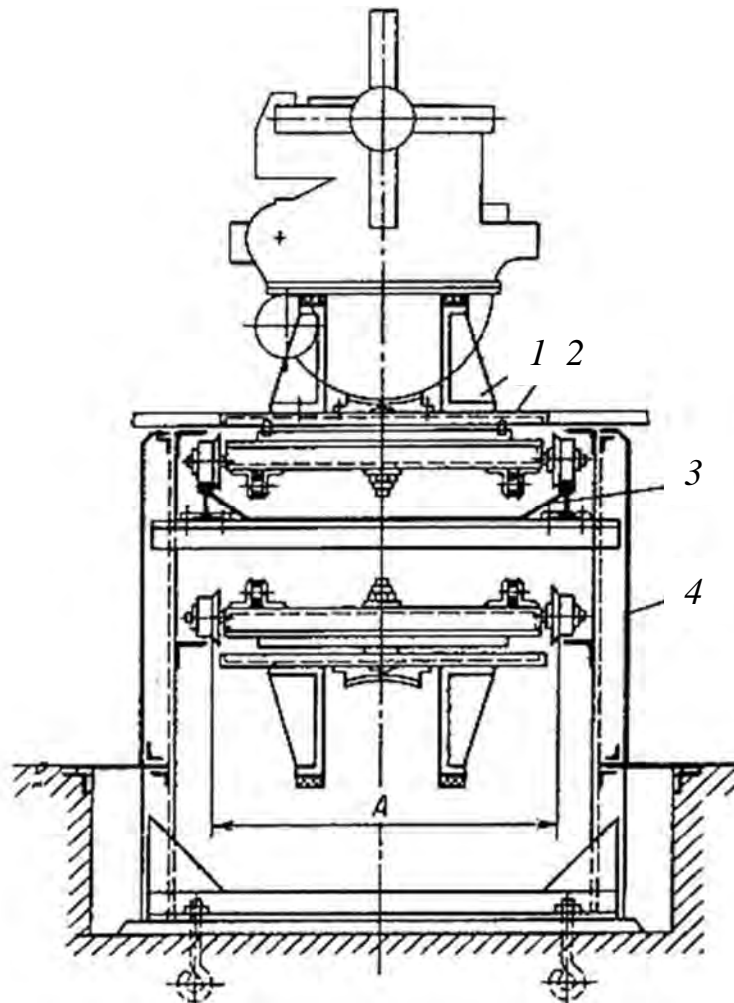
Конвейер с опрокидывающимися тележками для сборки автомобильных двигателей: 1 – установочный кондуктор; 2 – поворотное приспособление; 3 – сплошное перекрытие; 4 – ограждение
